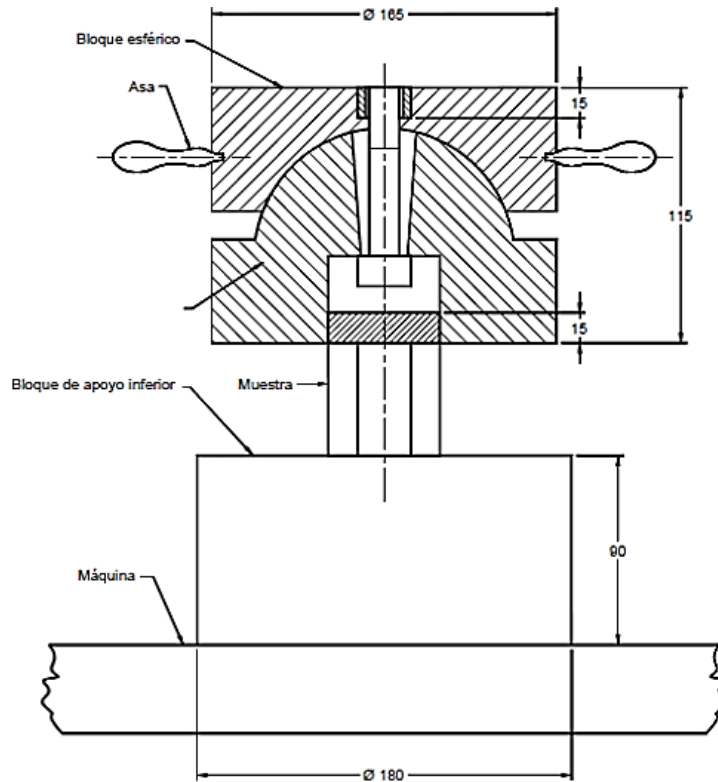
Detalle de máquina de compresión. Fuente: Norma Técnica Colombiana 5525
